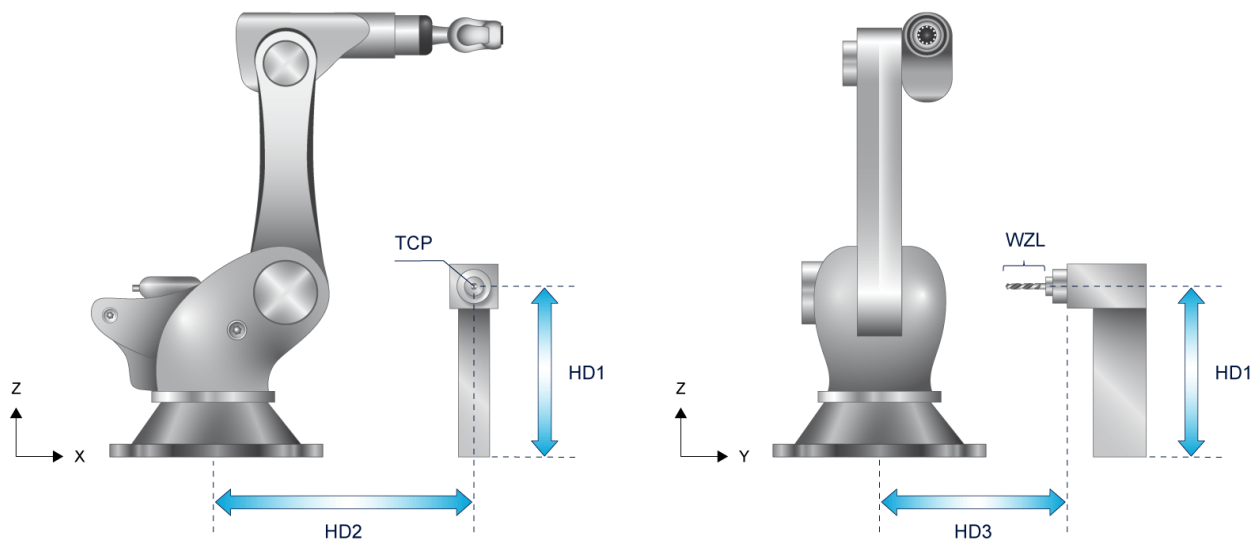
Werkzeugversätze des fest positionierten Werkzeuges
